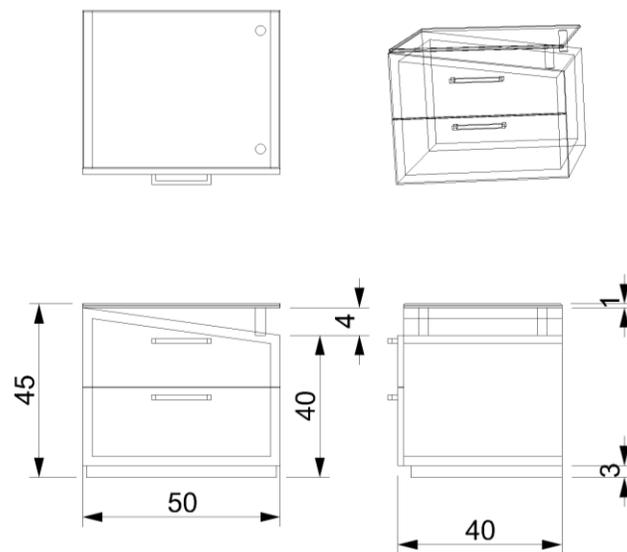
Antecedente Planos y Detalles Técnicos Nochero Eko
